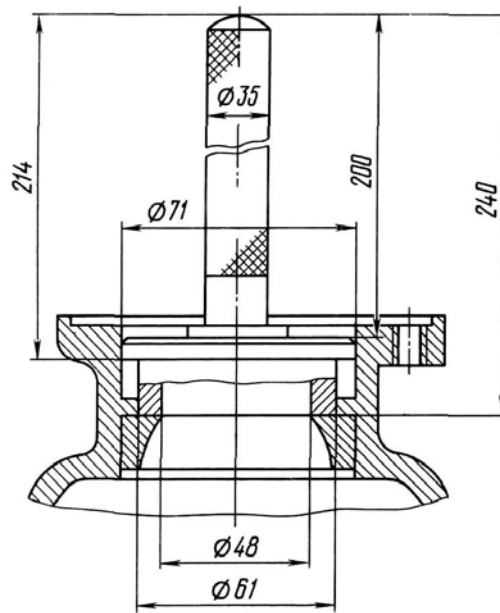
Выпрессовка наружной обоймы сферического подшипника
